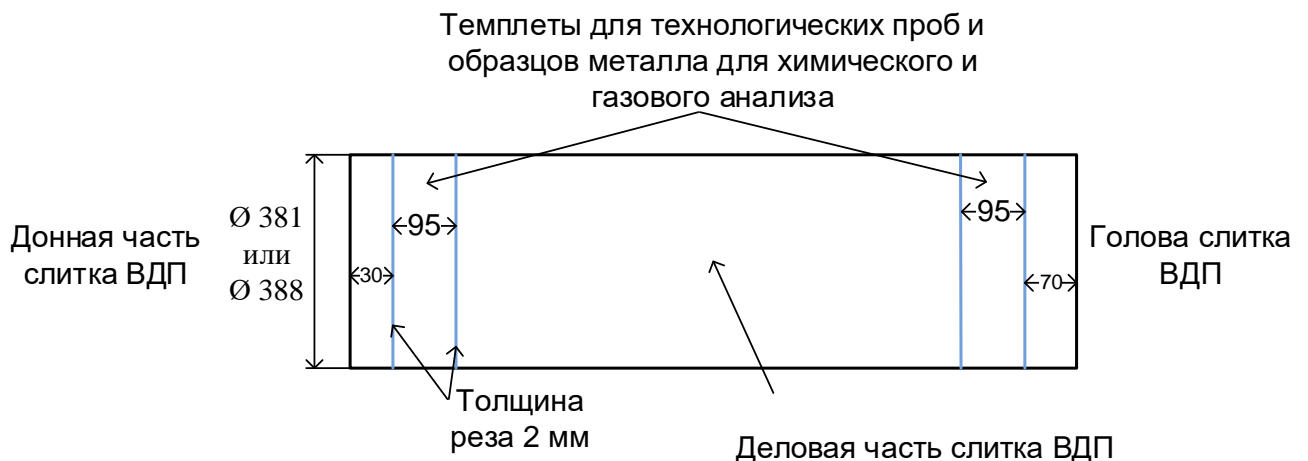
Схема порезки опытного слитка ВДП сплава Inconel 718
